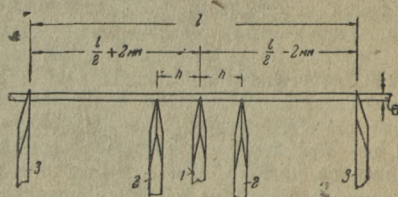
Схема расположения резачков в приспособлении к токарному станку
